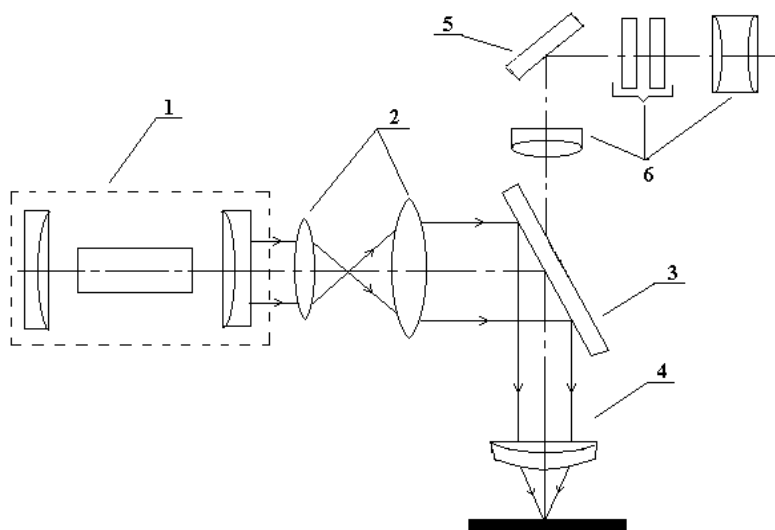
Оптическая схема установки для лазерной сварки
